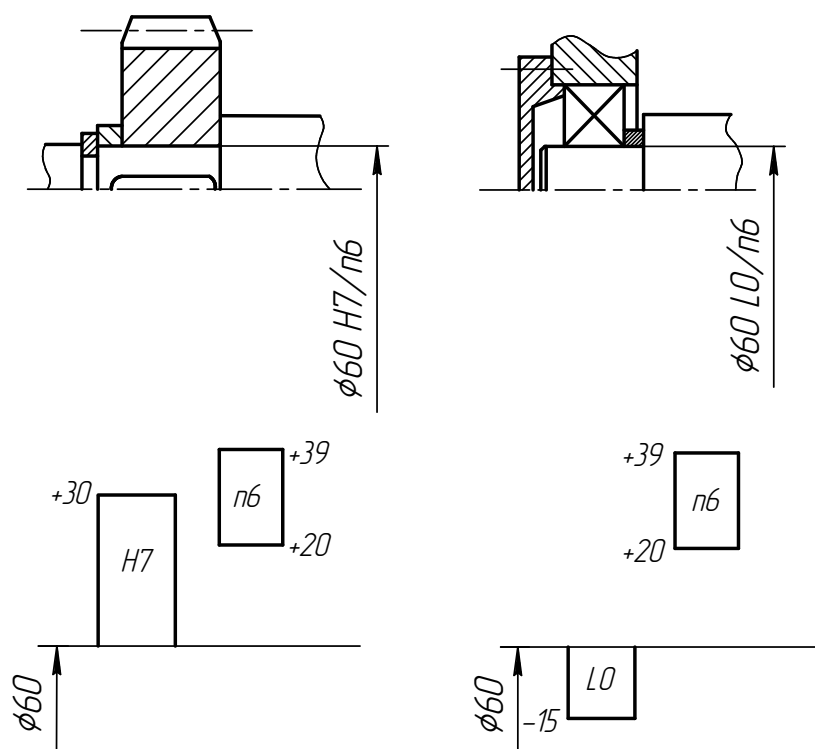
Схемы расположения полей допусков гладкого цилиндрического соединения (а) и соединения внутреннего кольца подшипника качения с валом (б)
